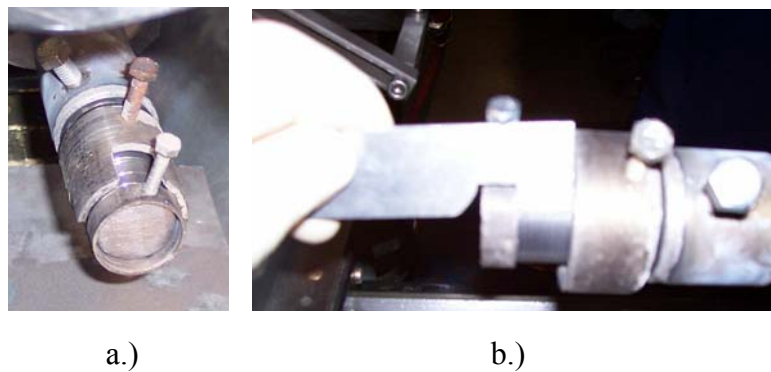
Dimensionado del Recubrimiento: a.) Colocación de Piezas Moldes y b.) Ajuste de la Altura con el Calibre.
